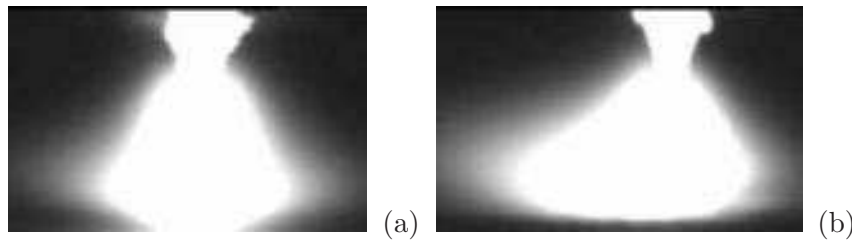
Vue de côté de l'arc électrique en soudage TIG (a) et soudage A-TIG ( $SiO_2$ ) (b) de l'aluminium A1050
